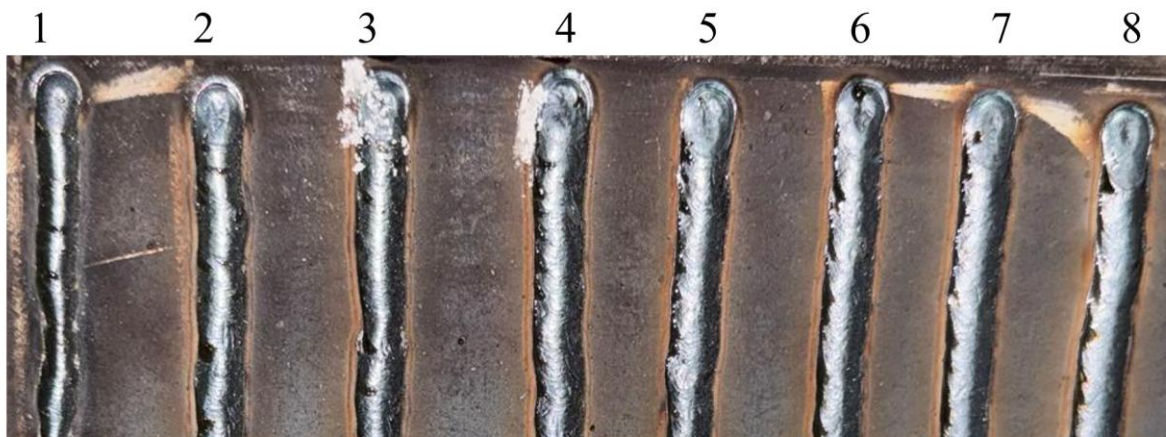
Полуавтоматическая наплавка проволокой марки СВ08Г2С
